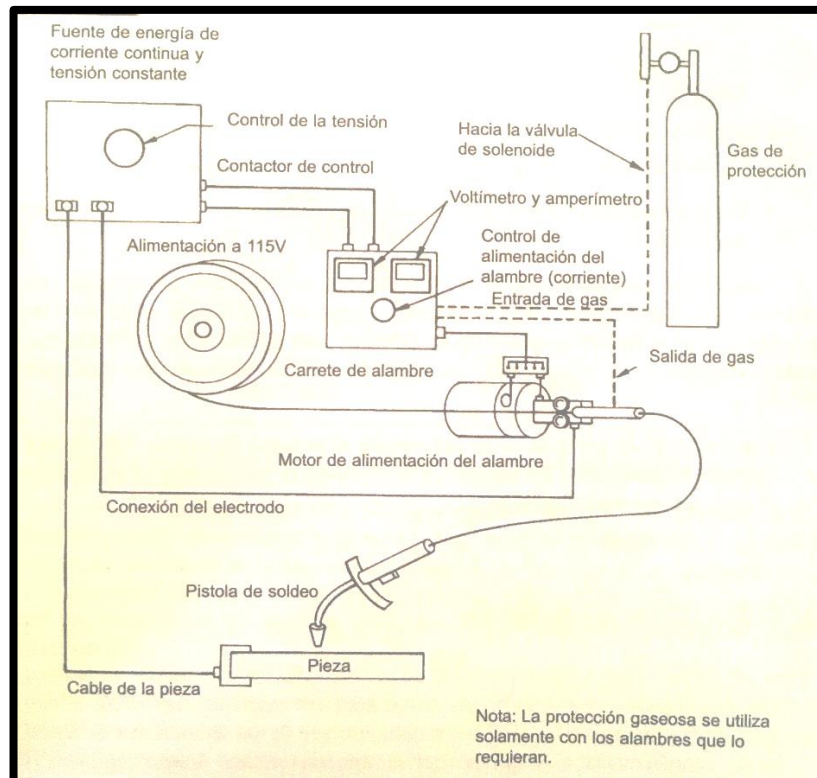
Equipo para el soldeo por arco con alambre tubular. Tomada del Manual del soldador
